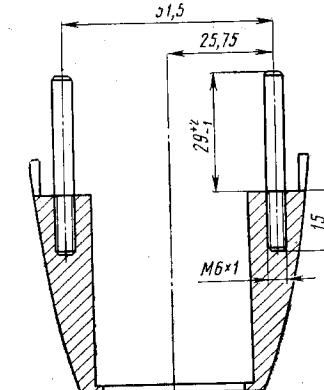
Размеры при ремонте корпуса фонаря освещения заднего номерного знака методом постановки ремонтной шпильки
